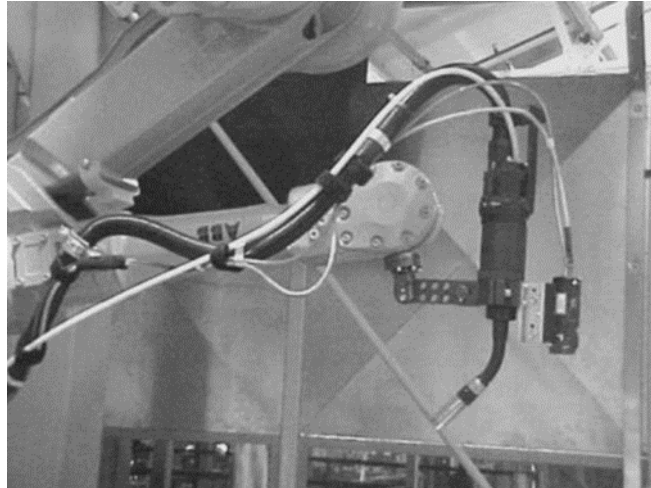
ABB 2400–16 Robô com Tocha de Soldagem MIG e o Sensor de Soldagem OST CSS montado na extremidade do braço (HKS Prozesstechnik 2013) [10]
